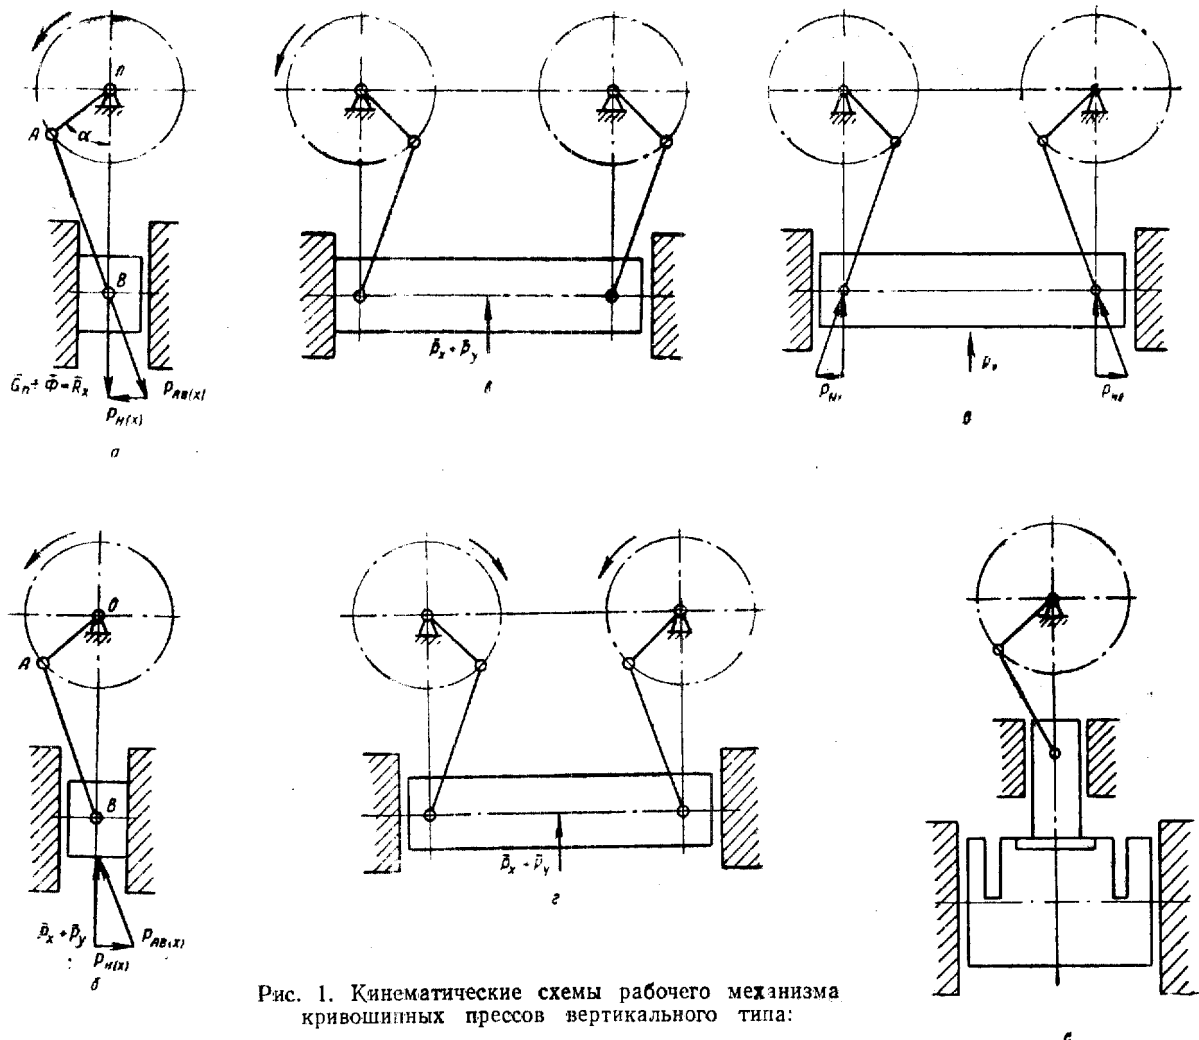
Кинематические схемы рабочего механизма кривошипных прессов вертикального типа:
